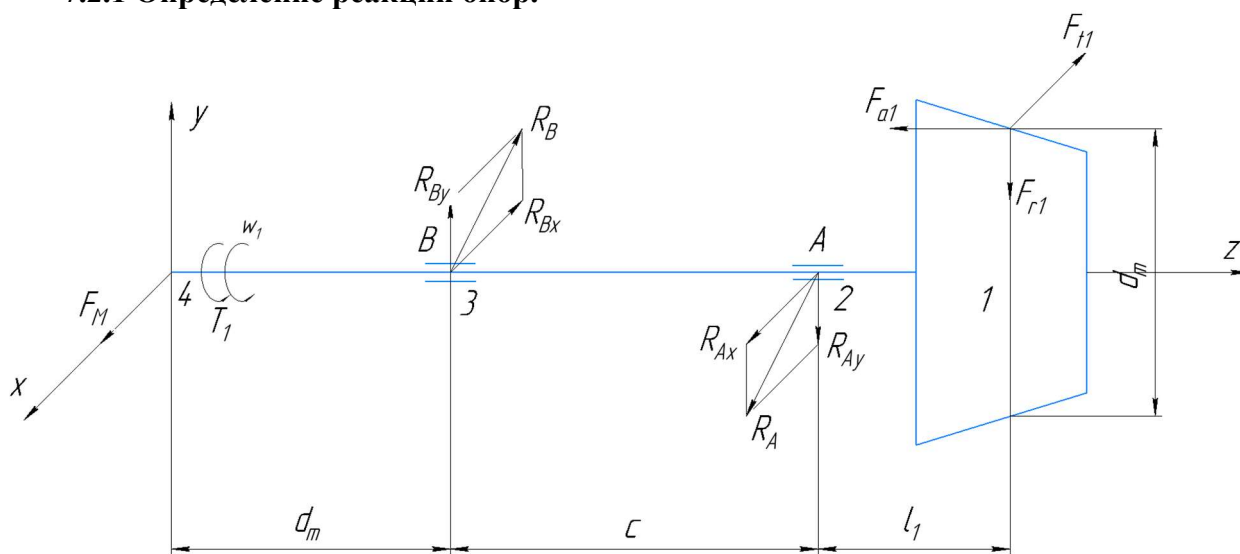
Схема нагружения подшипников быстроходного вала.
